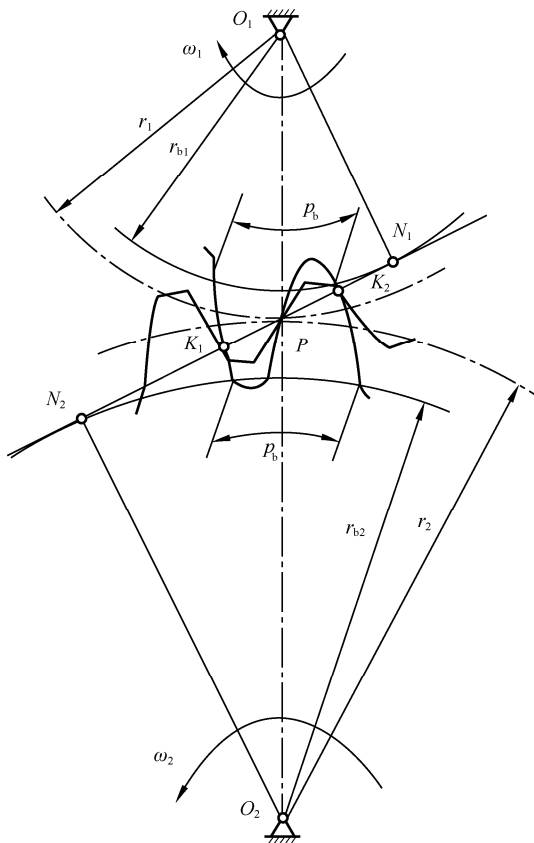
渐开线直齿圆柱齿轮正确啮合的条件
